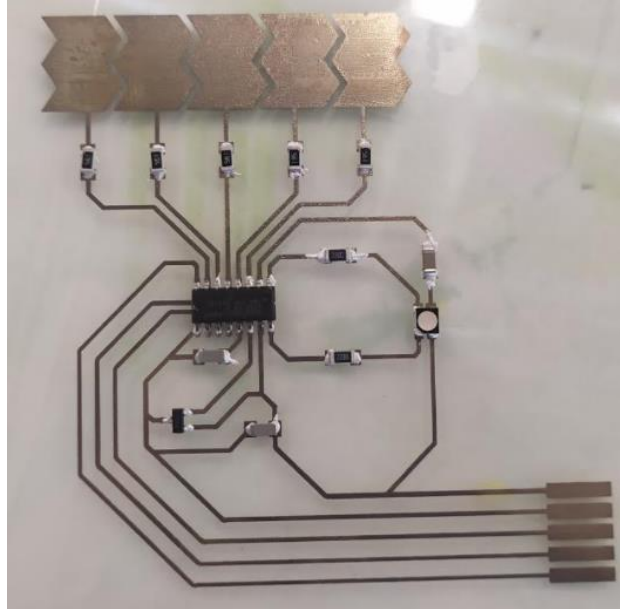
Dispositivo soldado mediante adhesivo de soldar
